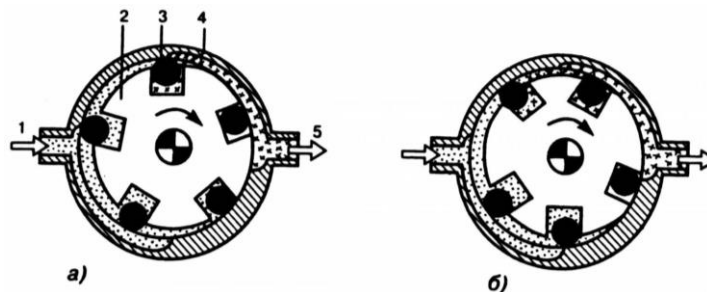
Схема роботи насоса: а - всмоктування палива; б - нагнітання палива; 1 - вхід палива; 2 - ротор насоса; 3 - ролики; 4 - опорна поверхня роликів; 5 - вихід палива.
